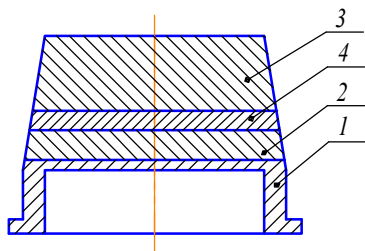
Конструкция четырехслойного СВС-прессованного катода:
